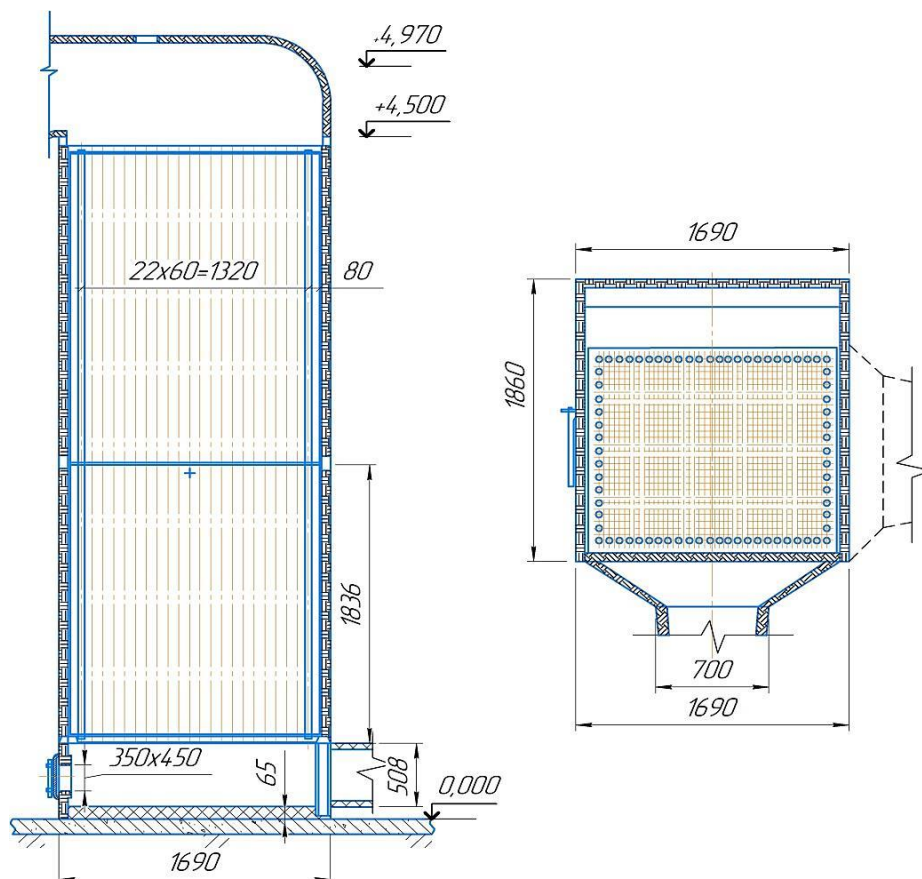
Конструкция воздухоподогревателя ВП-О-300
